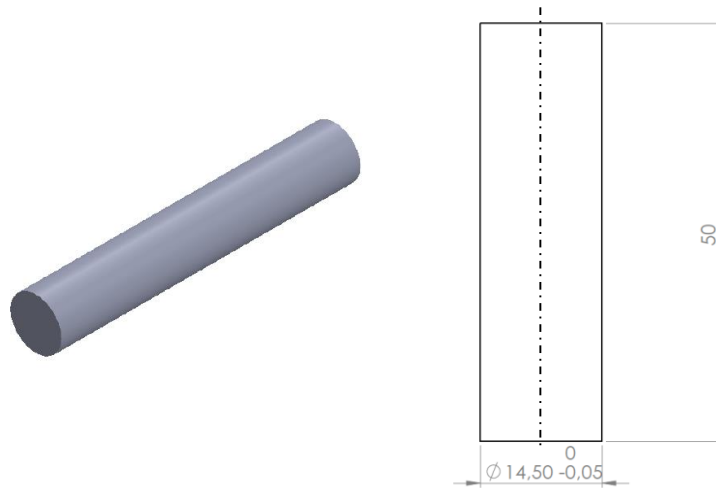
Technische Zeichnung der Rohlinge für das Fließpressen
